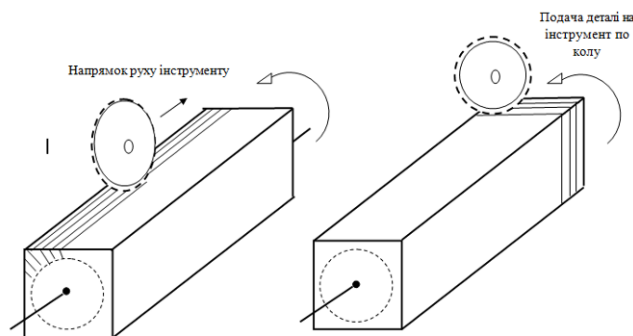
Схеми обробки заготовок тіл обертання при профільному фрезеруванні на верстатах з ЧПК.
